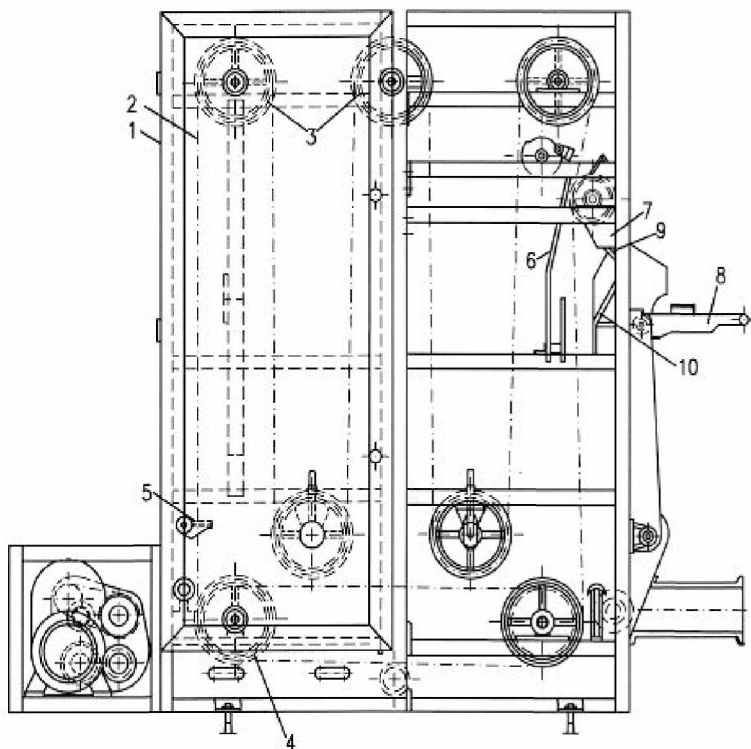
Шафа з колісковим конвеєром для попереднього вистоювання: 1 - шафа; 2 - дволанцюговий колісковий конвеєр; 3 - зірочки; 4 - привідні зірочки; 5 - колиски; 6 - напрямна планка; 7 - лотки; 8 - приймальний транспортер; 9 - поворотна планка; 10 - лоток.
